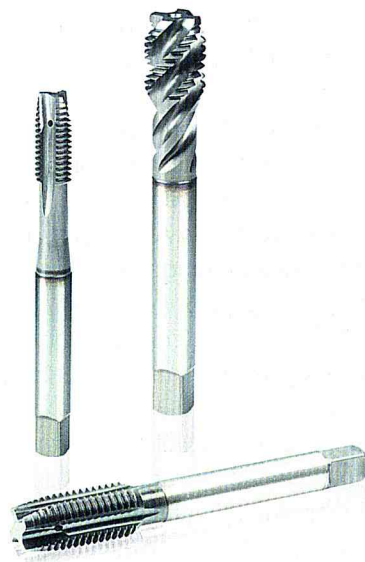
Um auch bei rostfreien Stählen, die bei der Bearbeitung häufig zum „Klemmen“ neigen, Gewindetiefen bis 3xD prozesssicher realisieren zu können, hat die Wexo Präzisionswerkzeuge GmbH eigens einen Gewindebohrer für schwer zerspanbare Werkstoffe entwickelt (Werkbilder: WEXO Präzisionswerkzeuge GmbH, Bad Homburg)
